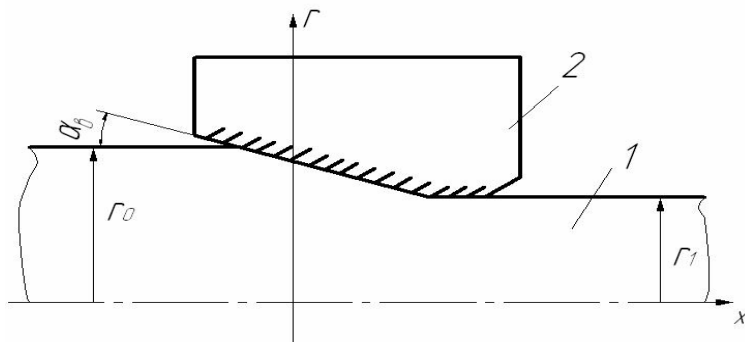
Схема волочения: 1 – композиционная заготовка, 2 – матрица-волокна
